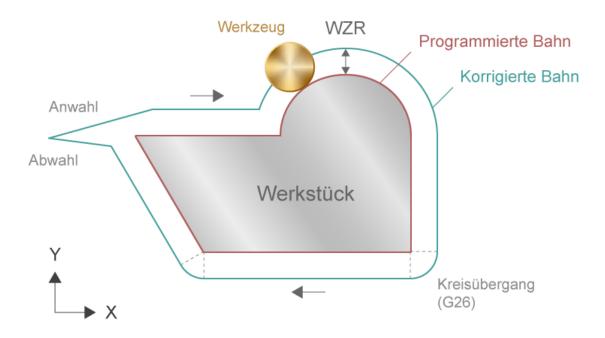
Werkzeugradiuskorrektur - Werkzeugradiusbahn
